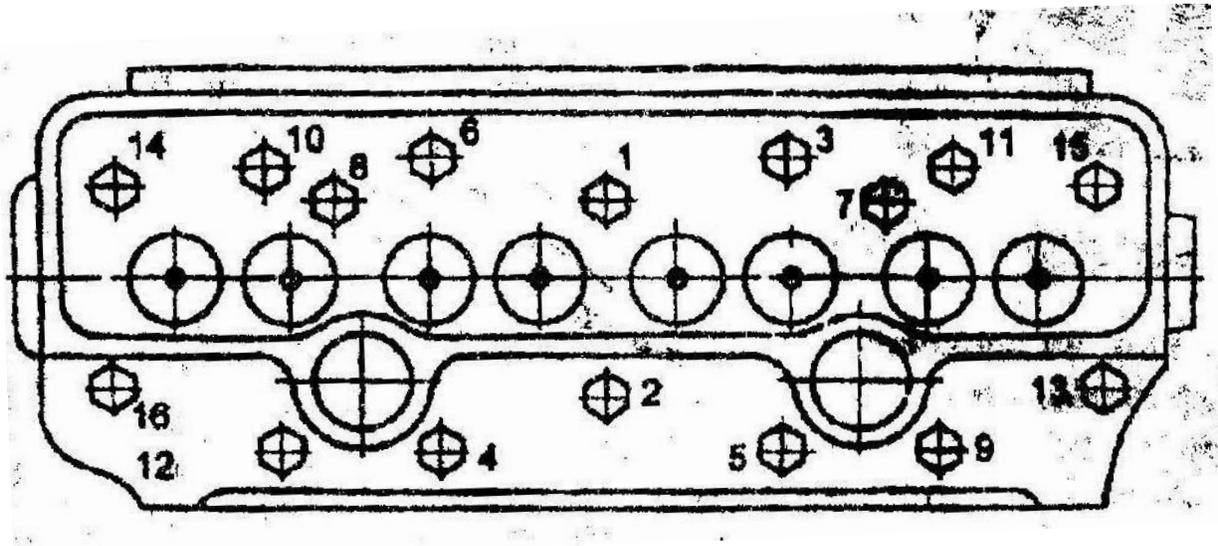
Схема последовательности затяжки болтов крепления головки цилиндров
